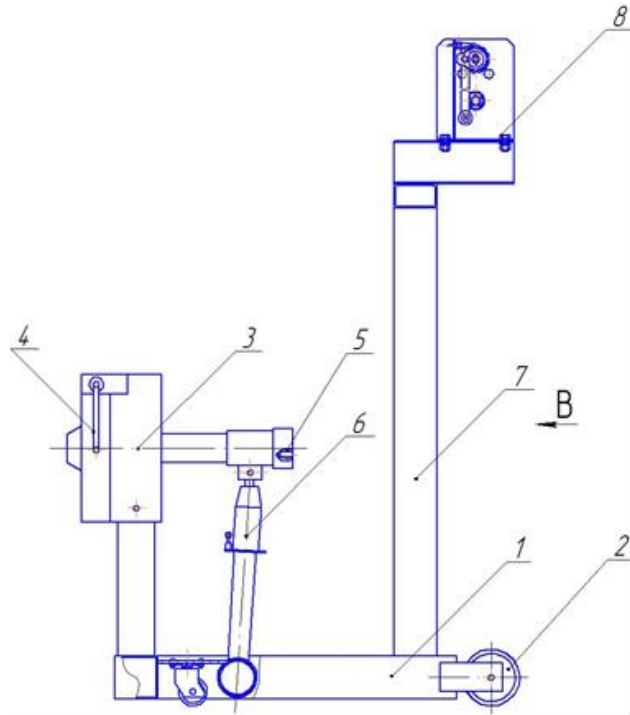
Стенд для розбирання-збирання двигунів: 1 – рама, 2 – колесо, 3 – черв'ячний редуктор, 4 – рукоятка, 5 – плита кріплення двигуна, 6 – домкрат гідравлічний, 7 – стійка лебідки, 8 – лебідка ручна.
